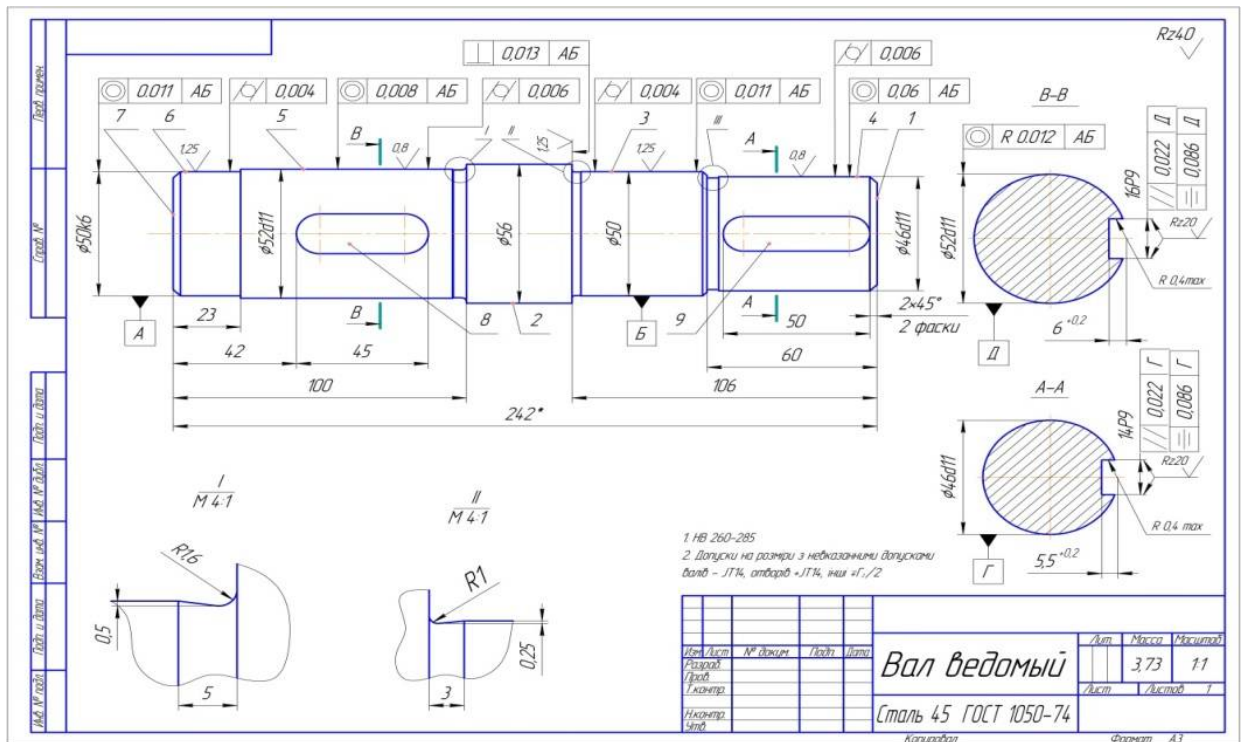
Робоче креслення деталі “Вал” з позначенням усіх поверхонь, що піддаються механічній обробці
